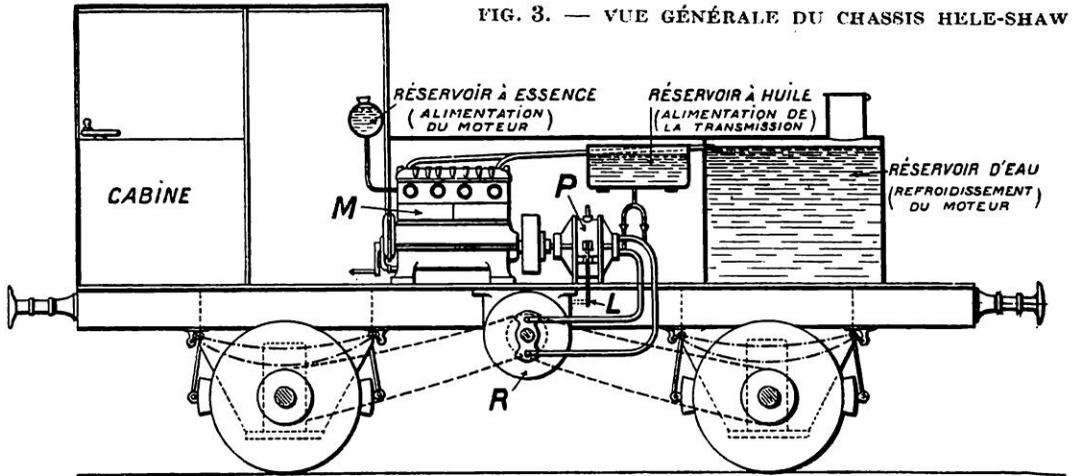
VUE GÉNÉRALE DU CHASSIS HELE-SHAW
